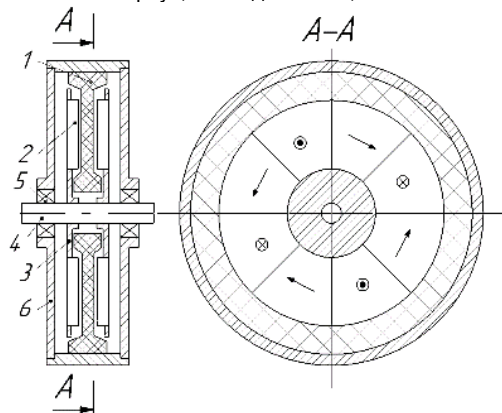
Двухсторонняя дисковая машина без магнитопроводов на статоре и роторе: 1 – обмотка беспазового безжелезного статора; 2 – ВПМ с магнитной сборкой Хальбаха; 3 – двойной ротор; 4 – вал; 5 – подшипники; 6 – корпус
